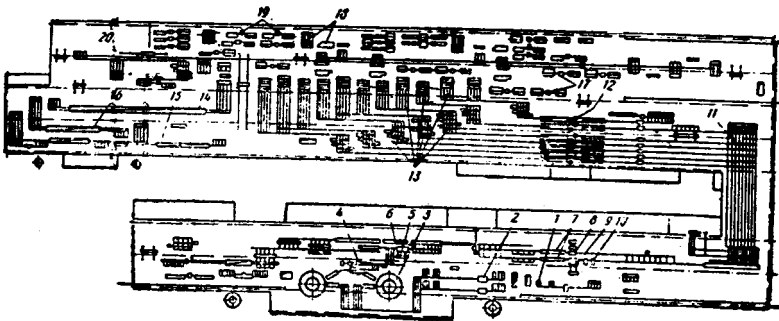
尼科波利南方钢管厂连轧管机组平面布置图
